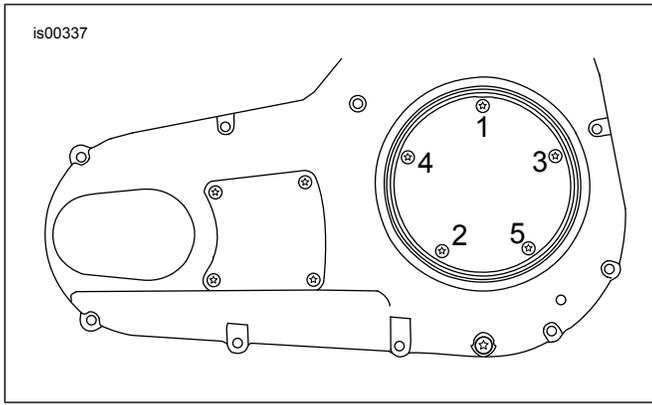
Seqüência de torque, tampa de inspeção da embreagem
